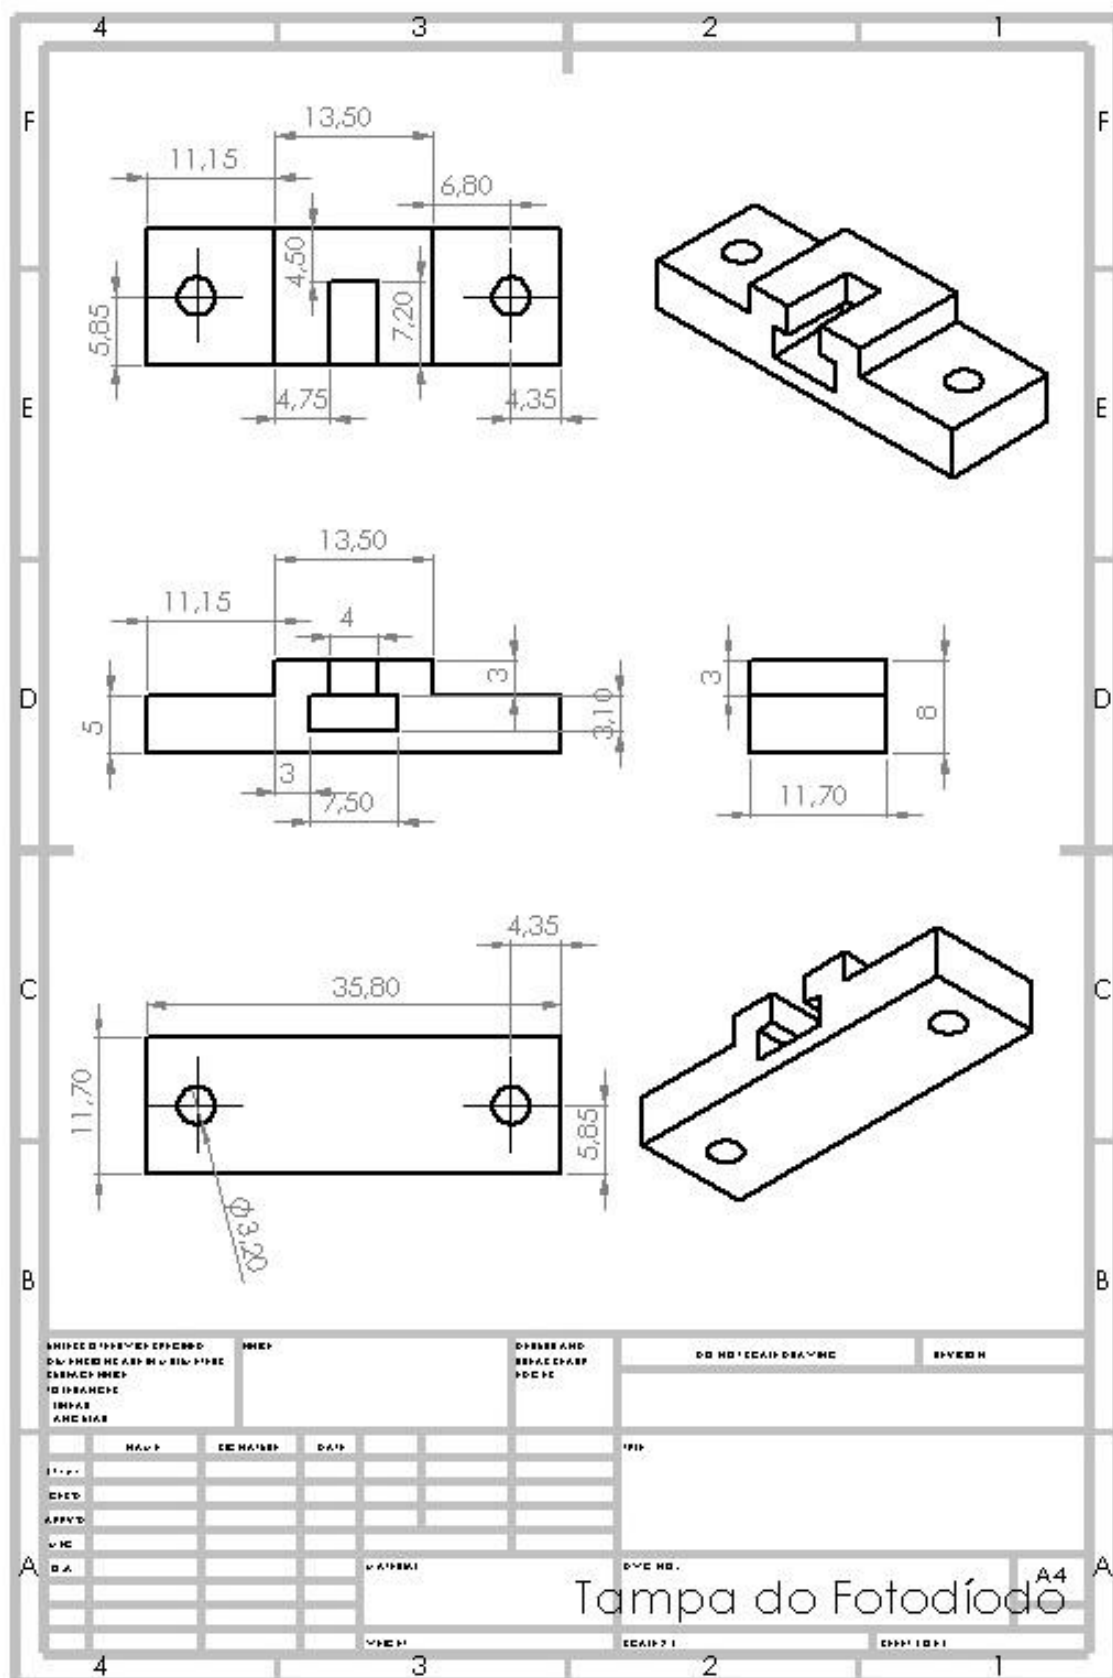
Desenho técnico da peça Tampa do Fotodíodo
